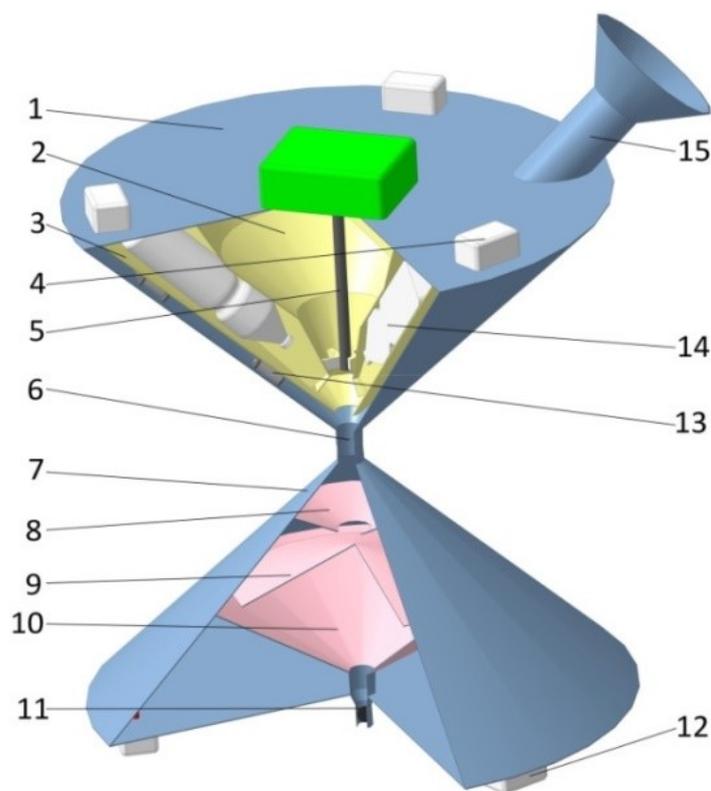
СВЧ-размораживатель с состыкованными вершинами конических резонаторов (патент № 2775137)
